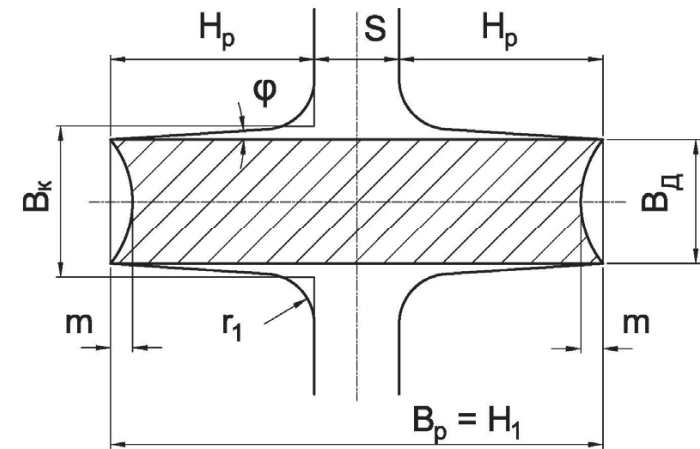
Конструкція ребрового калібру для прокатування штабової сталі
